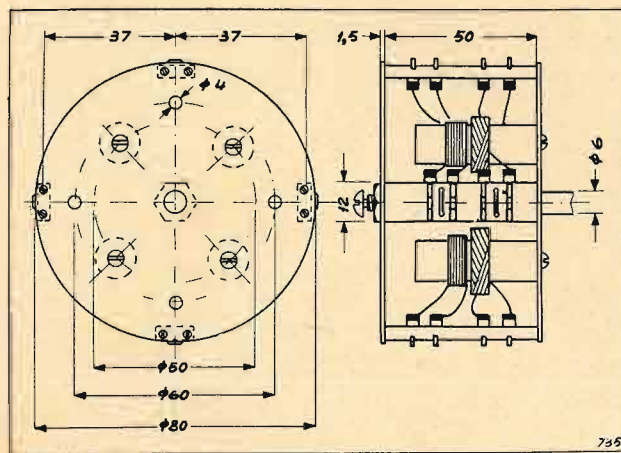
Disegno complessivo di un sistema a tamburo.
